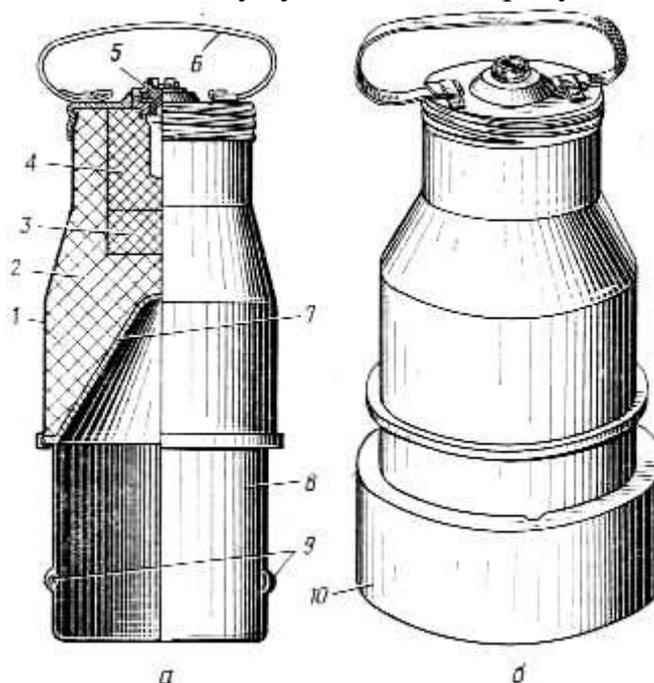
Загальний вигляд стандартного заряду СЗ-4П
